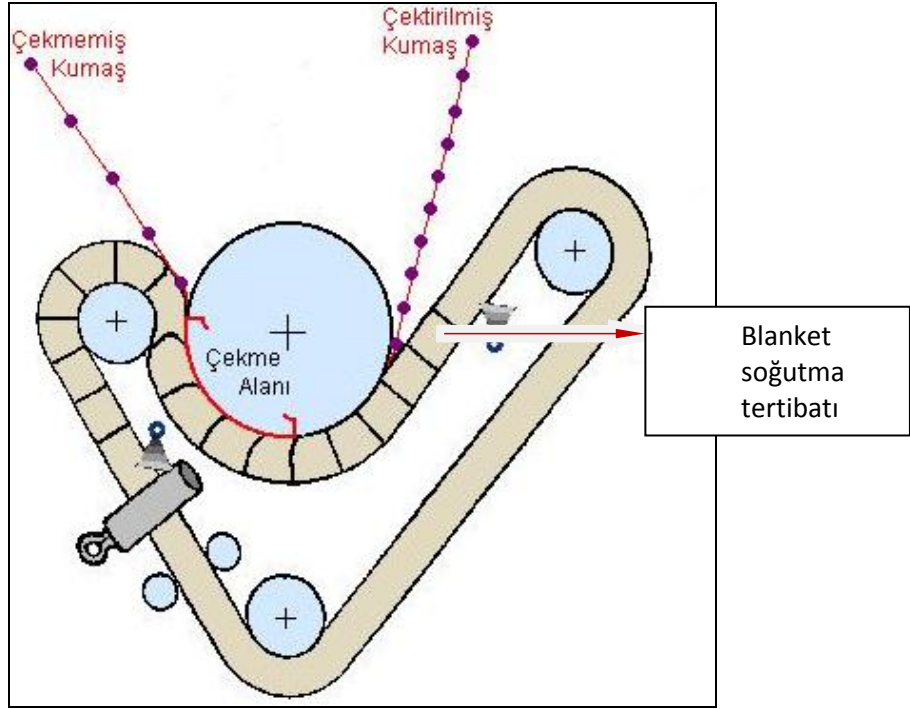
Sanfor makinesinde kauçuk blanket ile çelik silindir
